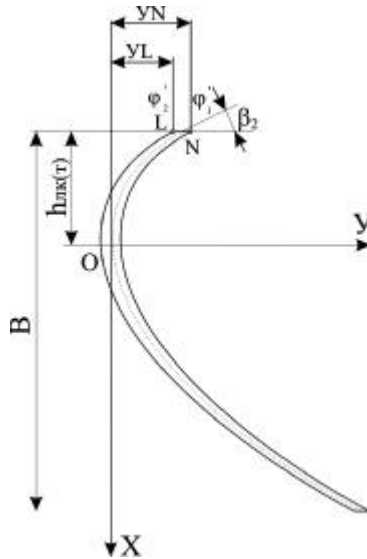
Образующая серповидного профиля колес турбокомпрессора
